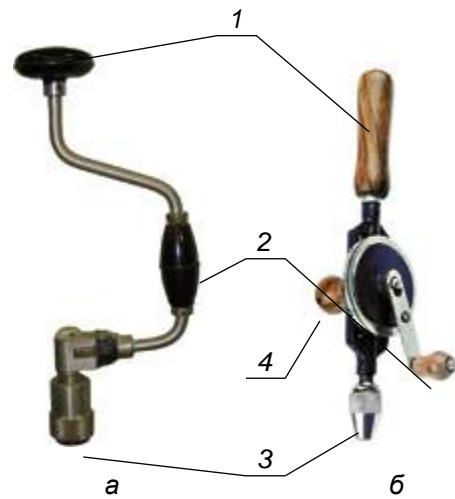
Ручные сверлильные инструменты: а – коловорот; б – ручная дрель. 1 – упорная ручка; 2 – ручка для вращения; 3 – патрон; 4 – ручка вспомогательная
